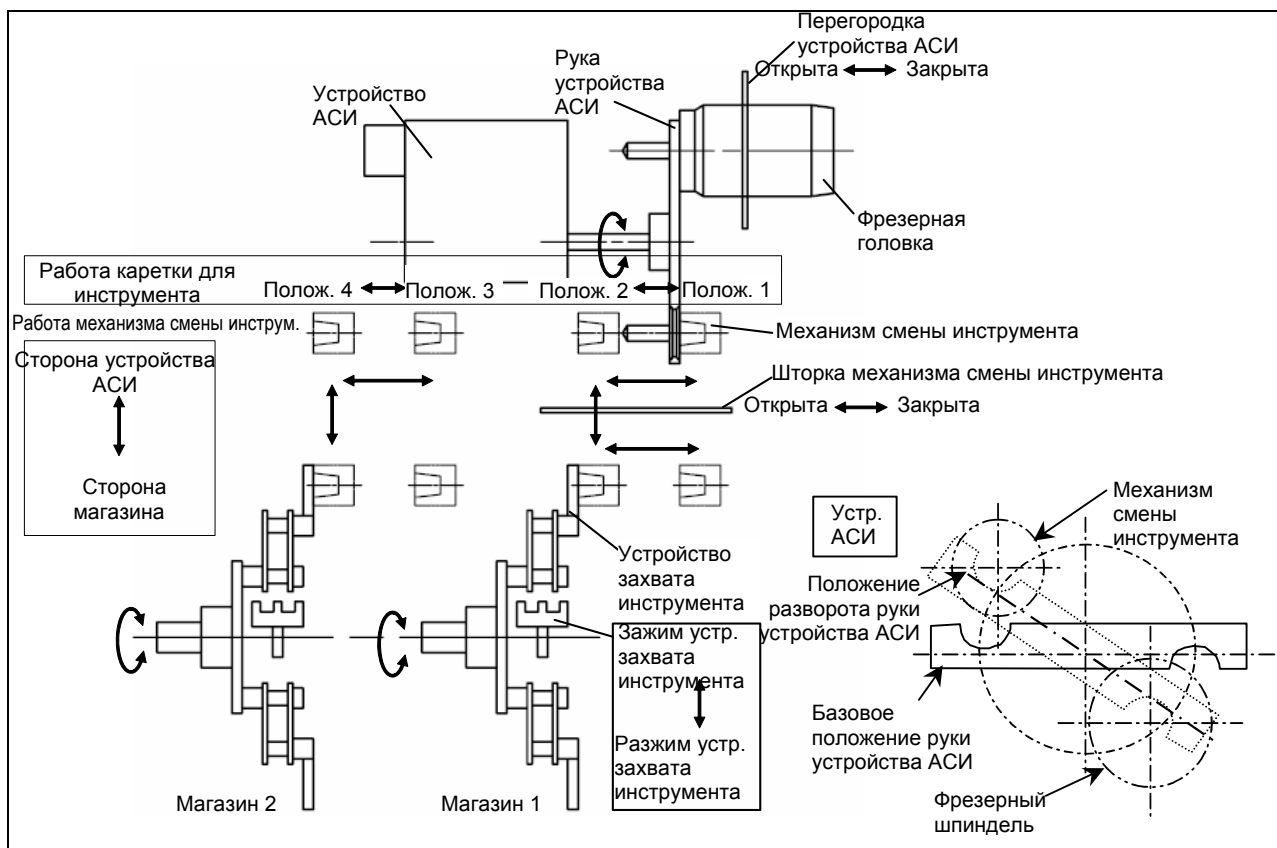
Базовые положения механизмов устройства АСИ (магазин на 72 инструмента)
